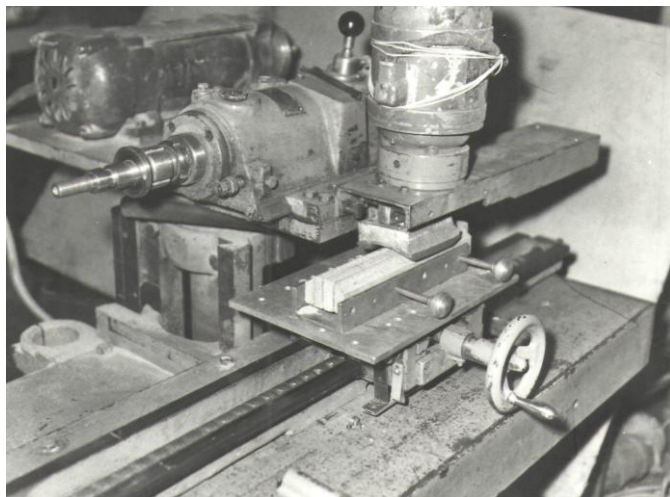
Загальний вигляд лабораторної установки із зворотно-поступальним рухом інструменту
